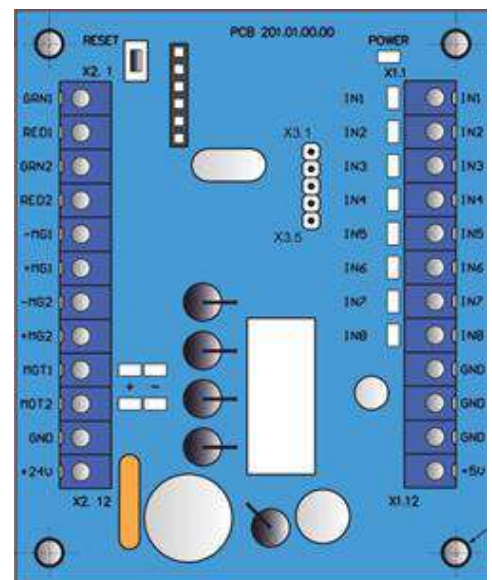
Зовнішній вигляд контролера моторизованого механізму PCB.201.01.00.00
